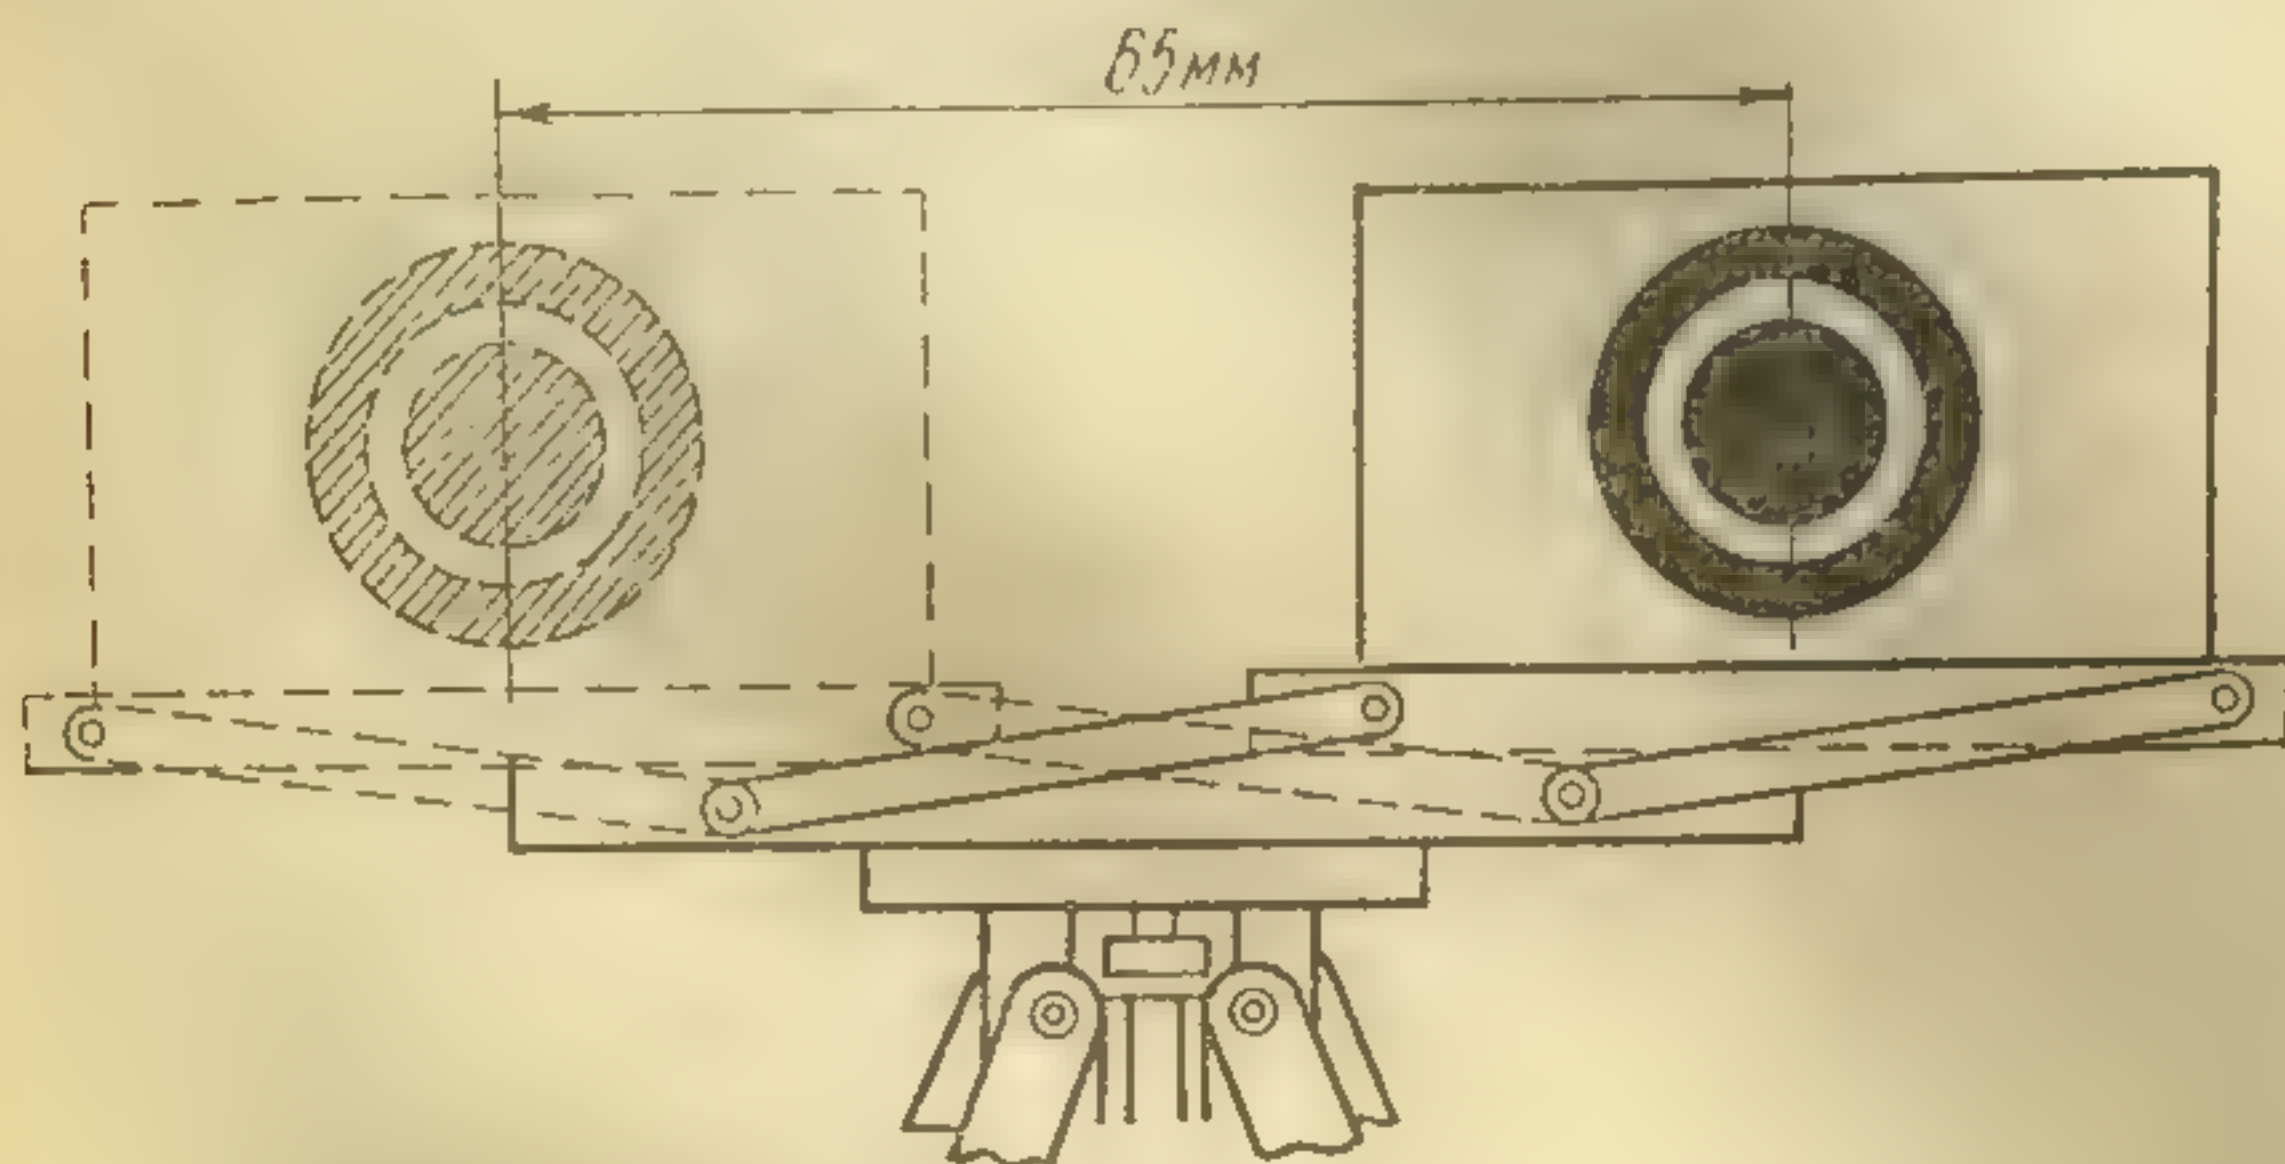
Приспособление для стереосъемки обычным фотоаппаратом.
